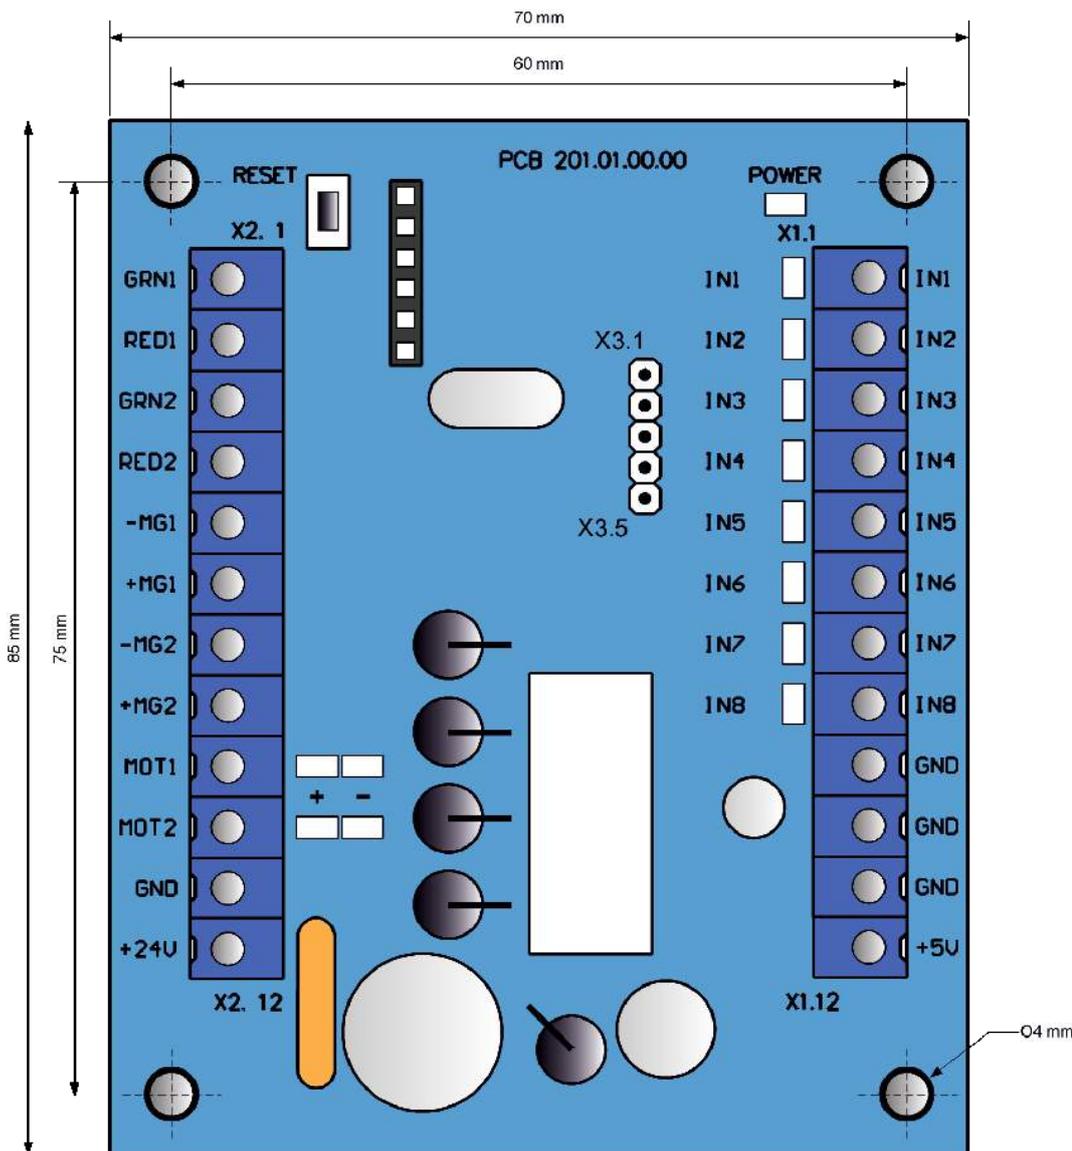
Внешний вид контроллера PCB.201.01.00.00
